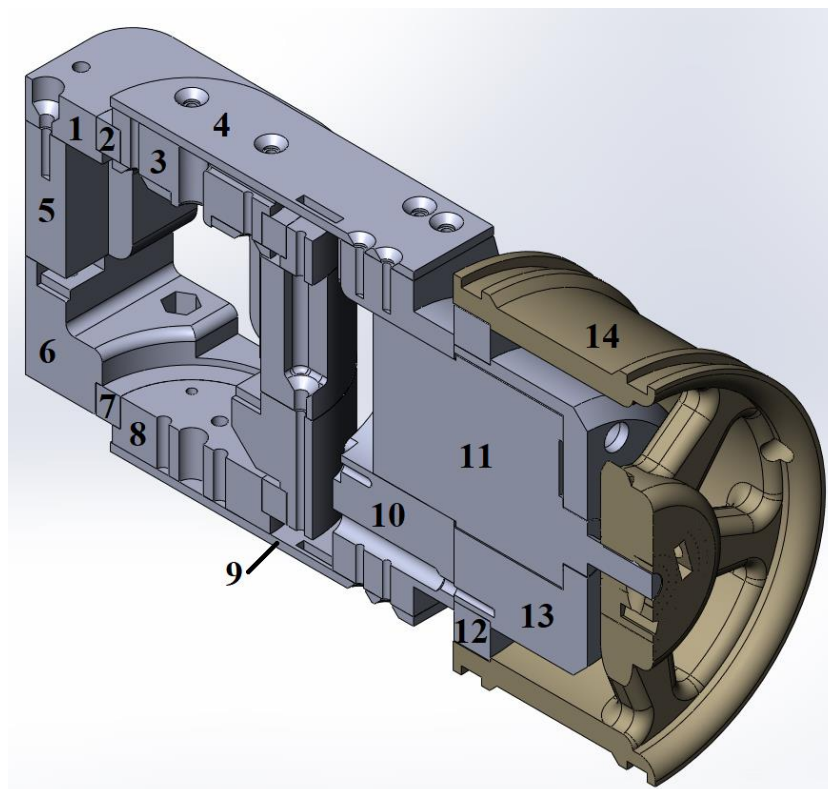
Модель поворотного узла в разрезе: 1 – крышка оболочки сервопривода; 2 – верхний подшипник; 3 – верхняя втулка; 4 – верхняя балка; 5 – корпус оболочки сервопривода; 6 – кронштейн сервопривода; 7 – нижний подшипник; 8 – нижняя втулка; 9 – нижняя балка; 10 – колесо мотор-колеса; 11 – двигатель постоянного тока (далее – ДПТ); 12 – подшипник мотор-колеса; 13 – стакан ДПТ; 14 – диск мотор-колеса
